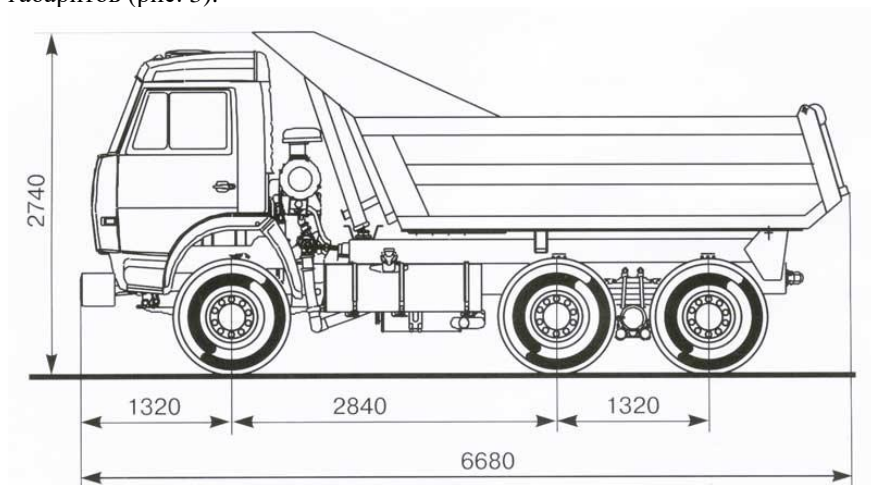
Общий вид автомобиля КАМАЗ-65115
